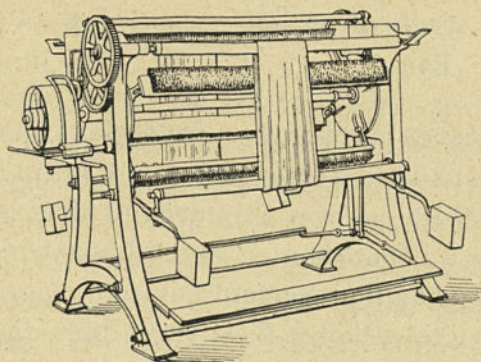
Machine à broser les fils (Zittauer M. F.).
